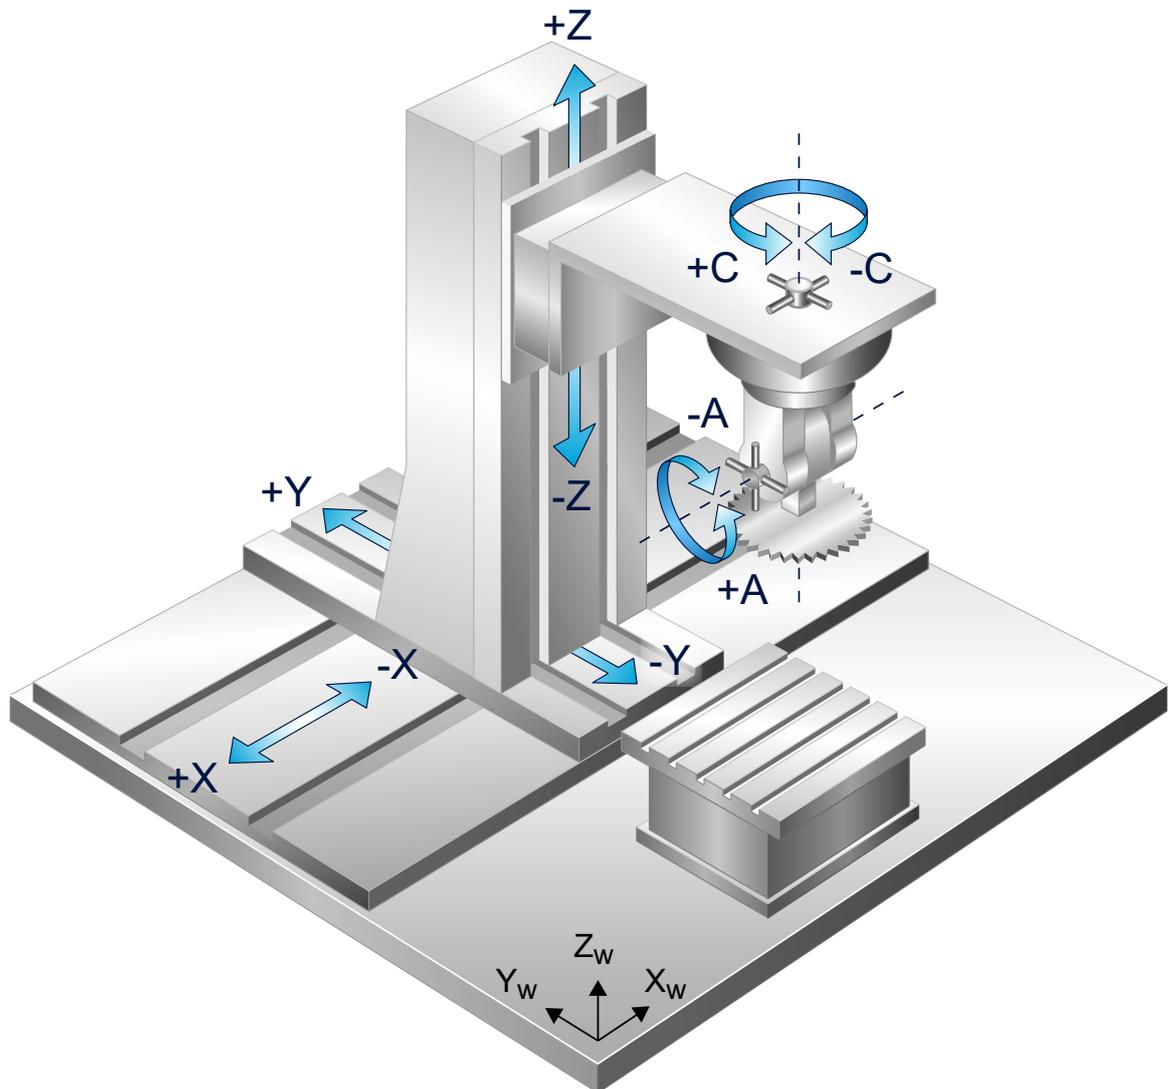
5-achsige Kinematik (Sägewerkzeug mit manuellen Hilfsachsen C und A)
